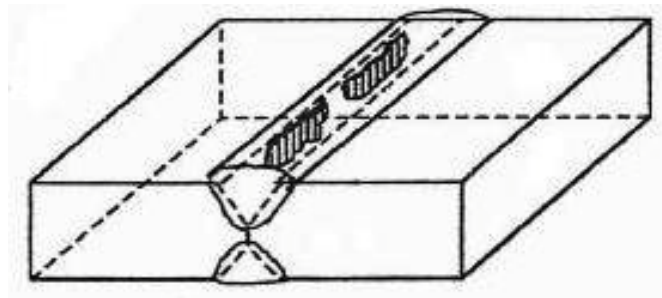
GRIETAS LONGITUDINALES
